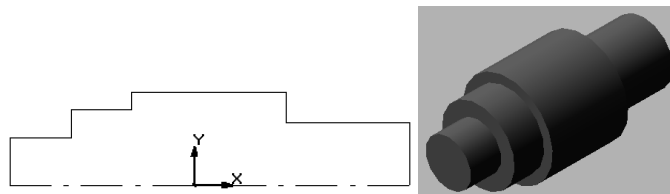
Ескіз і деталь типу «вал», утворена операцією обертання
